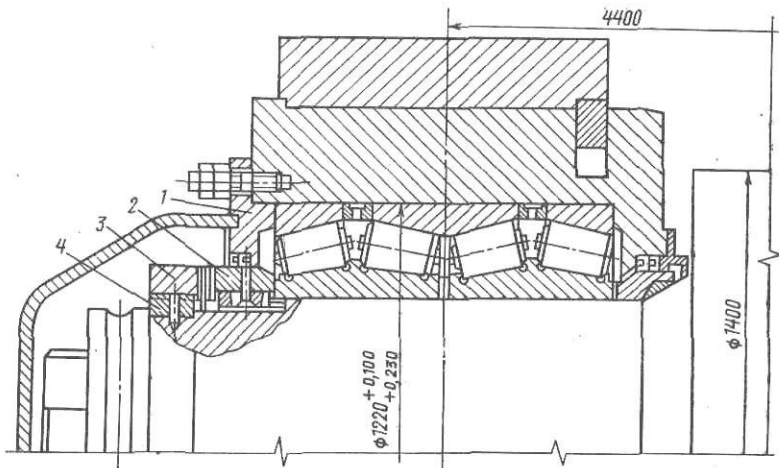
Установка опорного валка стана 2800 на роликовых конических подшипниках
